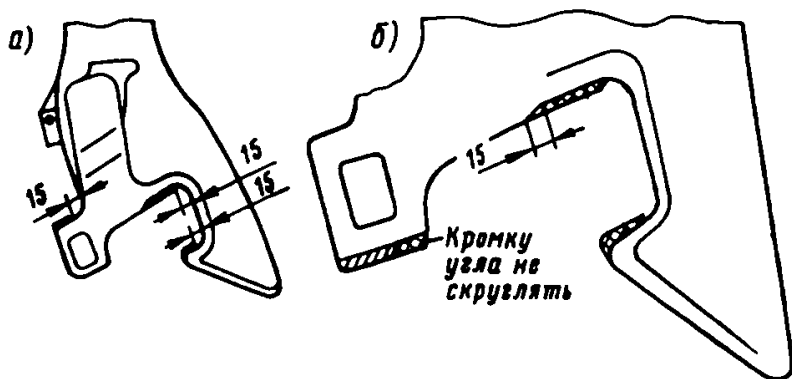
Требования к поверхностям контура зацепления корпуса автосцепки после их наплавки
